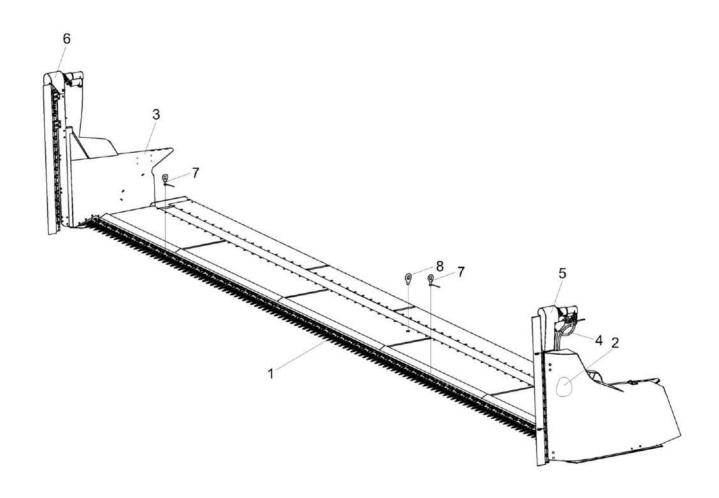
Приспособление для уборки рапса КЗК-9-1540000А (лист 1)
